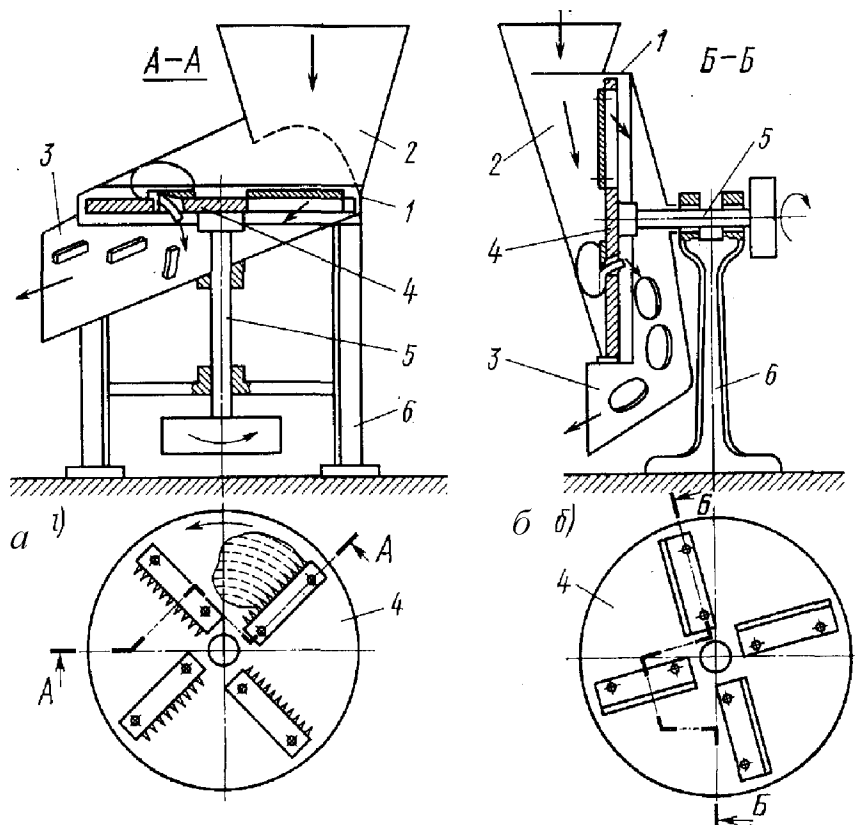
Схеми дискових овочерізок: а – з горизонтальним диском; б – з вертикальним диском; 1 – циліндр пустотілий; 2 – завантажувальний пристрій; 3 – розвантажувальний лотік; 4 – опорний диск; 5 – вал привідний; 6 – станина
